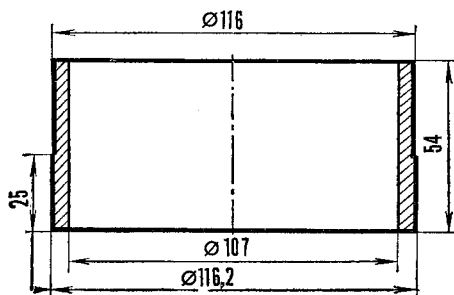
Вставка для картера ČZ-360 при установке коленчатого вала ČZ-250
